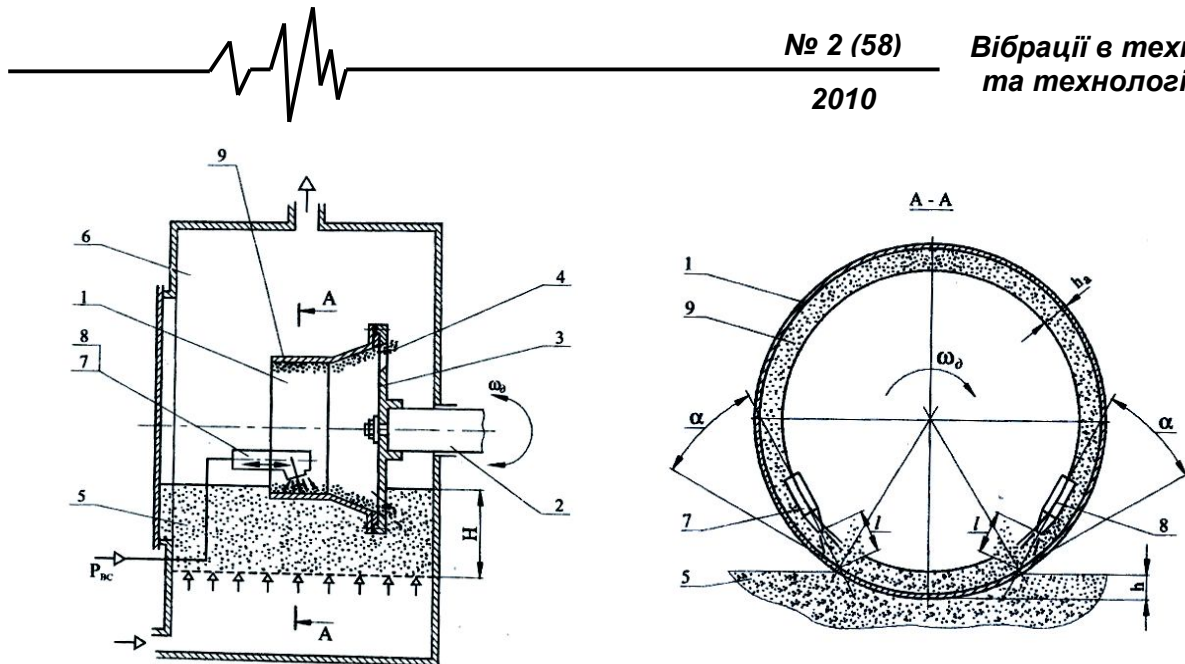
Схема турбоабразивных установок модели АПС-350Б и АПС-600А для обработки вала ротора КВД:
